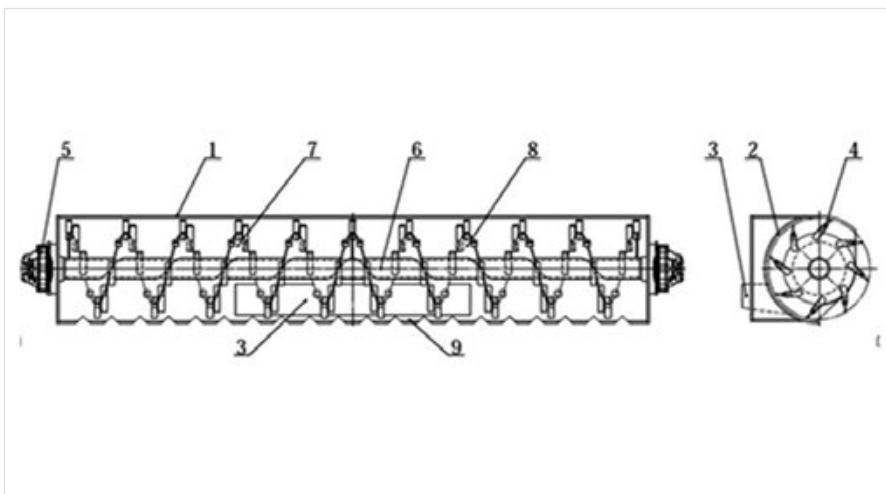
Грунтозаборное устройство фрезерно-шнекового типа со сменными режущими ножами
